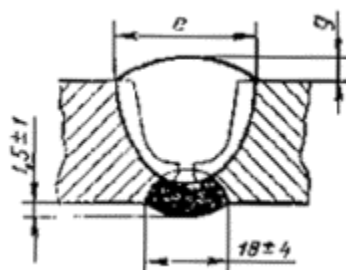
Конструктивные элементы сварного шва.
